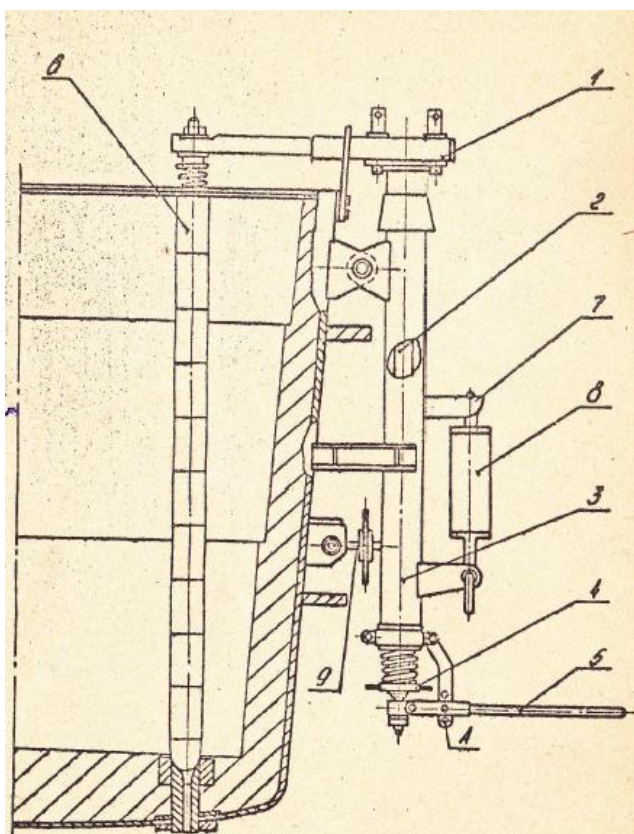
Стопорний пристрій сталерозливного ковша
